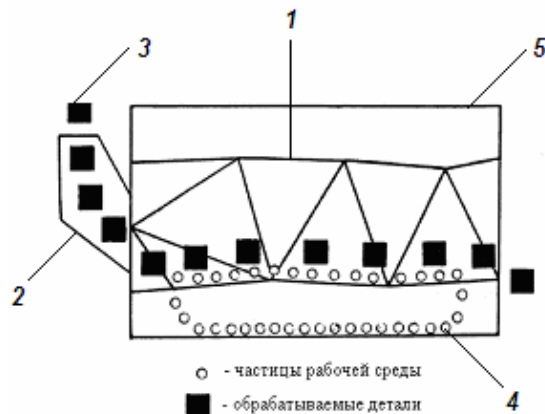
Схема движения обрабатываемых деталей и частиц рабочих сред в установке для непрерывной отделочно-зачистной обработки деталей
